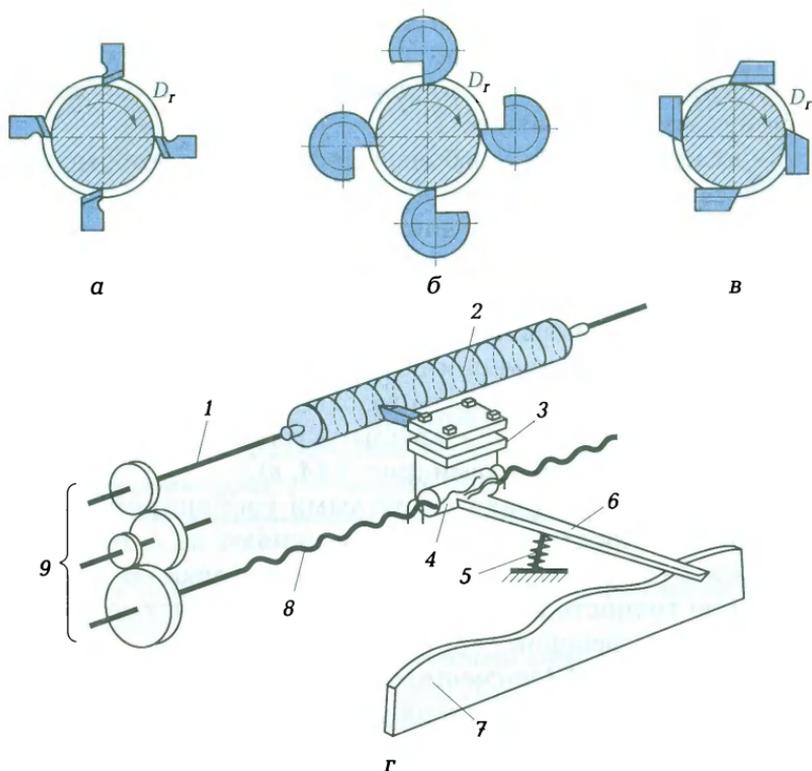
Схемы нарезания резьб на токарно-винторезном станке:
